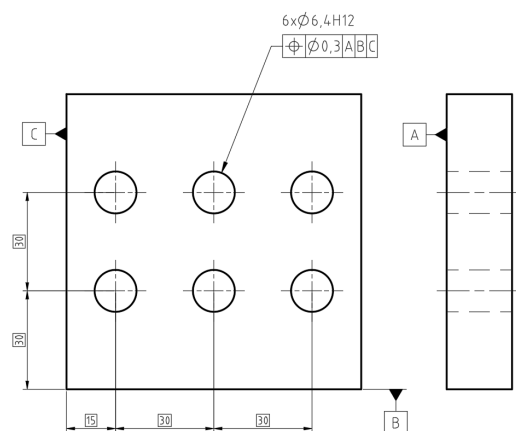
Rozdíl ve způsobu měření geometrických úchylek při záměně pořadí základen [3]
